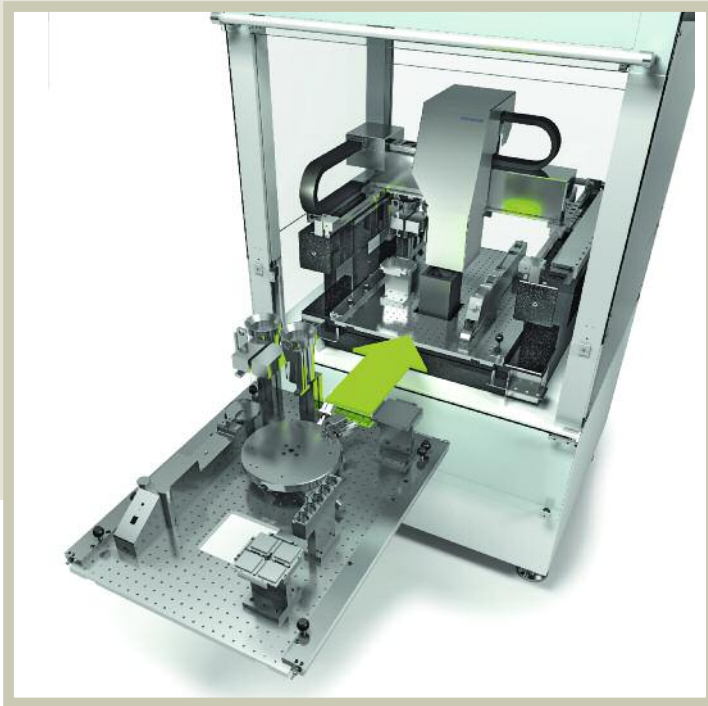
Auswechselbare Montageplatte für den schnellen Produktwechsel
